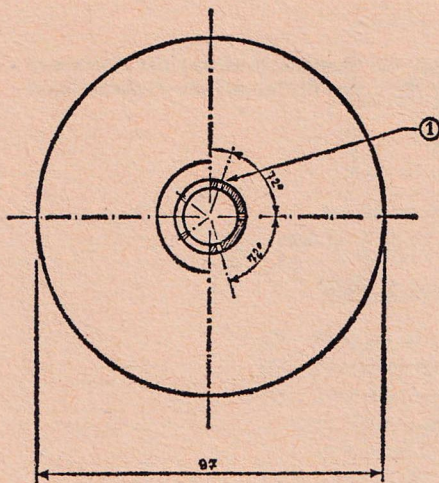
hohler Bronzezylinder, einseitig verschlossen;
